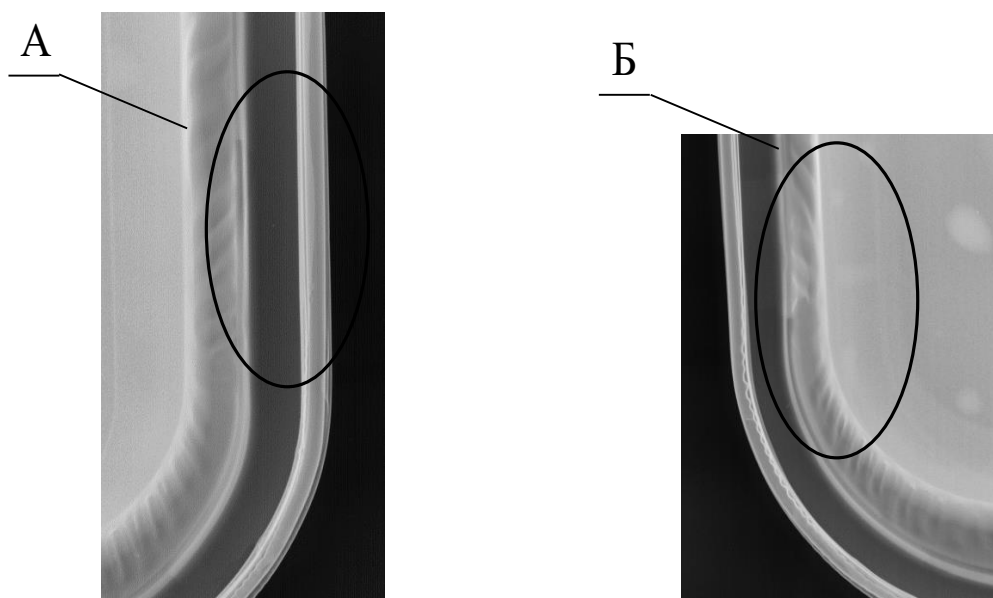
А и Б – выделенные области с нарушением соединения крышки с корпусом банки
